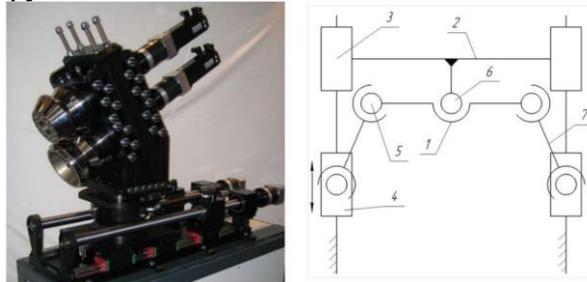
Установка 3D валковой формовки с параллельной кинематикой
